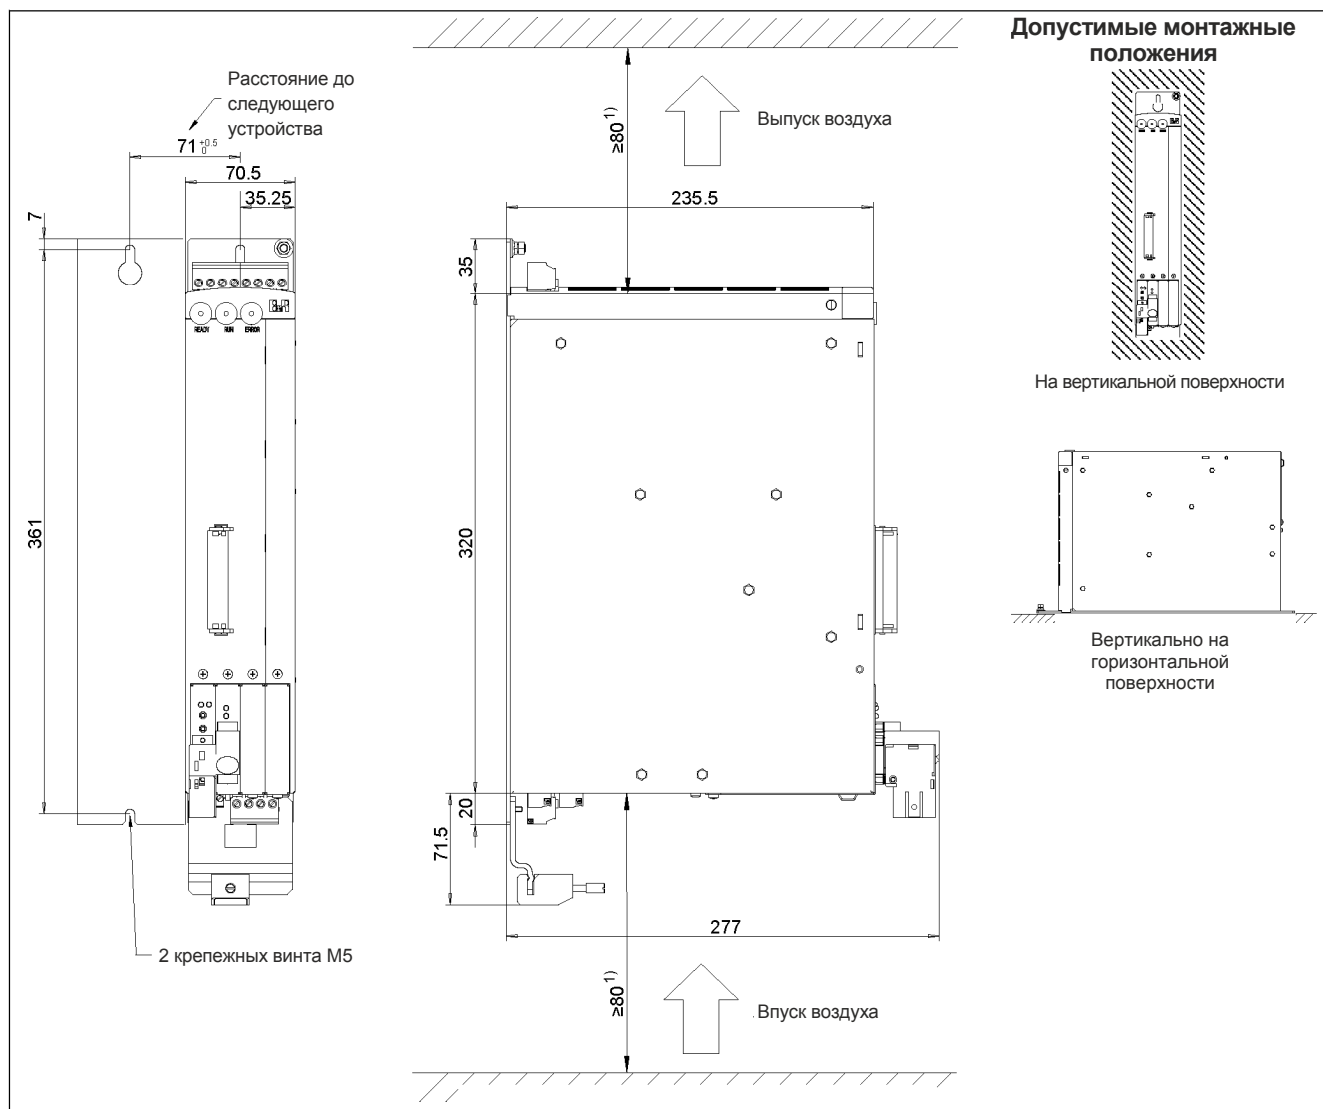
ACOPOS 1022, 1045, 1090 – Габаритный чертеж и монтажные размеры
